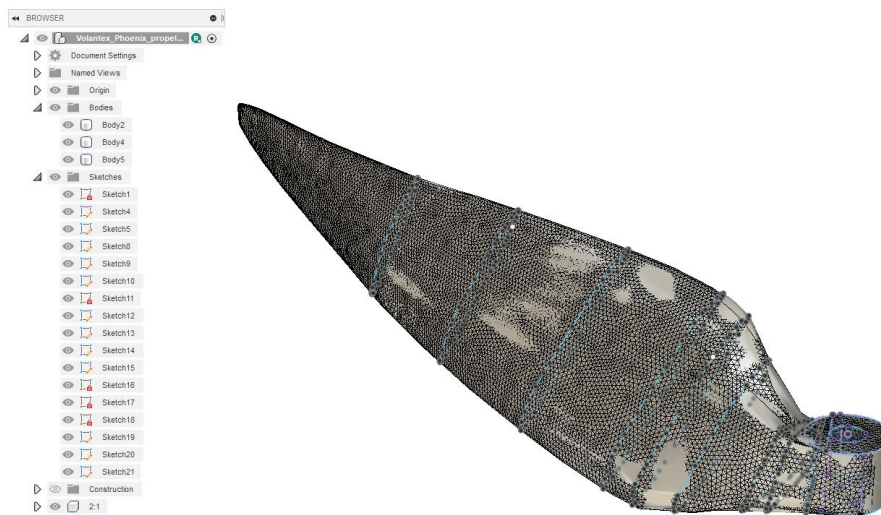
Реконструкция сечений для построения 3D-модели в CAD пакете Fusion 360
